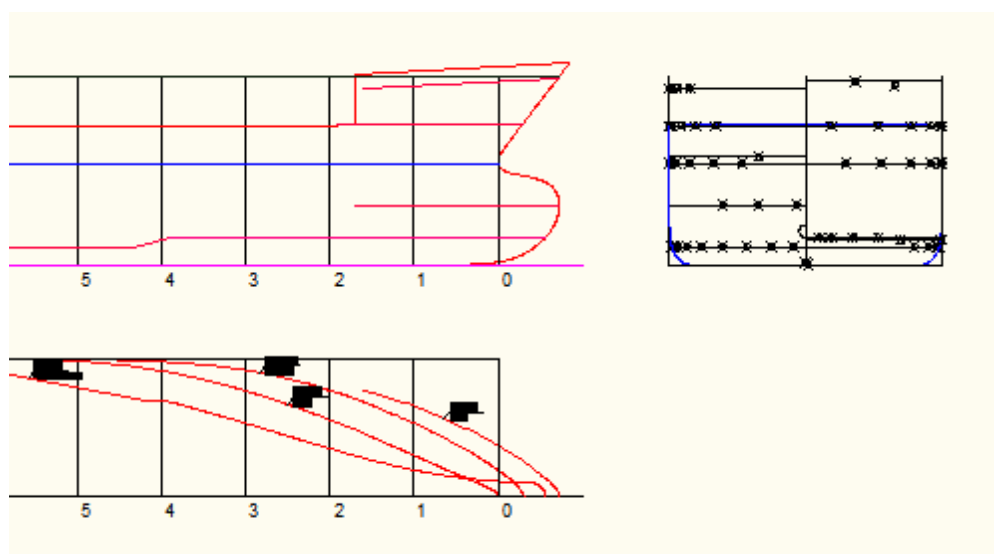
Реконструкции теоретического чертежа в AutoCAD
